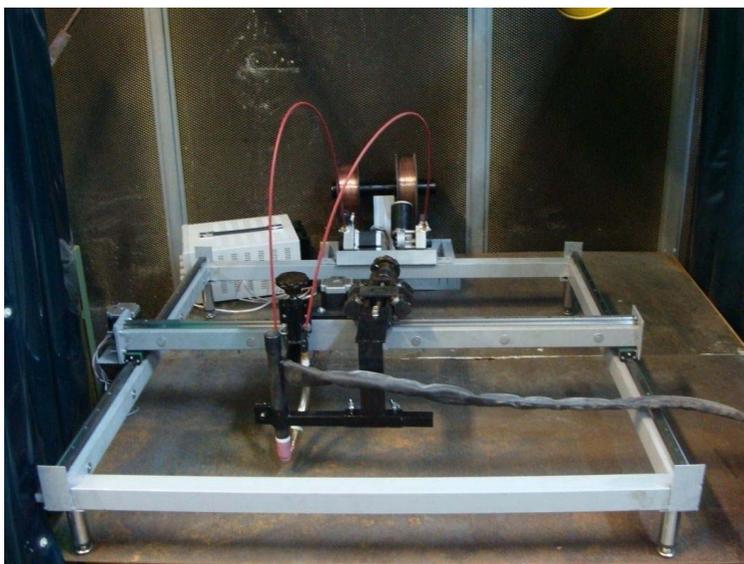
Установка для автоматической аргодуговой сварки
